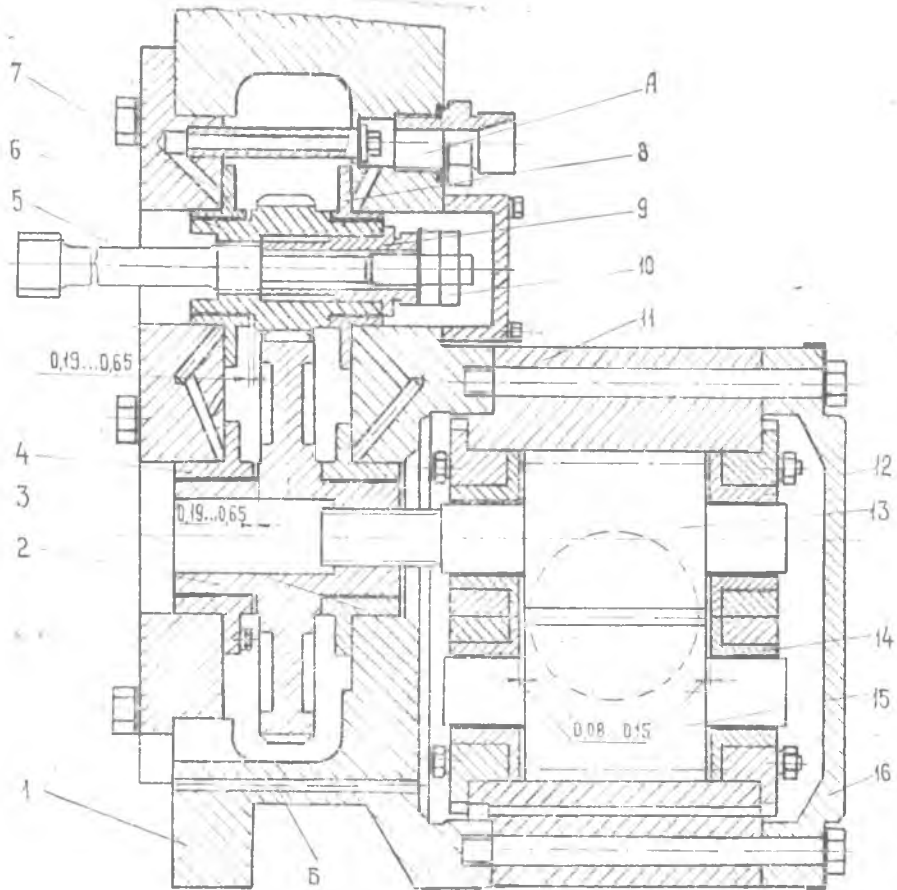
Блок маслонасоса: 1, 11 — корпус; 2 — шестерня; 3, 4, 7, 8, 12, 14 — подшипник; 5 — вал торсионный; 6 — вал-шестерня; 9 — гайка; 10 — контргайка; 13 — шестерня ведущая; 15 — шестерня ведомая; 16 — маслонасос
